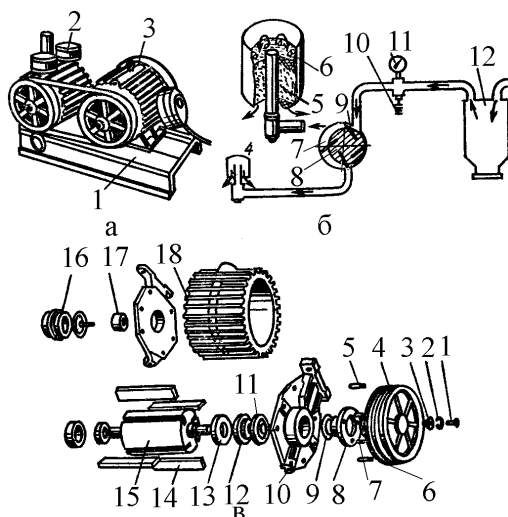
Установка вакуумная унифицированная УВУ-60/45: а – общий вид; б – схема работы; 1 – рама; 2 – масленка; 3 – электродвигатель; 4 – глушитель; 5 – стекловата; 6 – корпус глушителя; 7 – корпус; 8 – ротор; 9 – лопатки; 10 – вакуумный регулятор; 11 – вакуумметр; 12 – вакуум-баллон; в – сборочные единицы: 1 – болт; 2, 3, 13 – шайба; 4 – шкив; 5 – штифт; 6 – шпонка; 7 – винт; 8, 10 – крышка; 9 – кольцо; 11 – манжета; 12 – шарикоподшипник; 14 – лопатка; 15 – ротор; 16 – колпачок; 17 – втулка; 18 – корпус.
